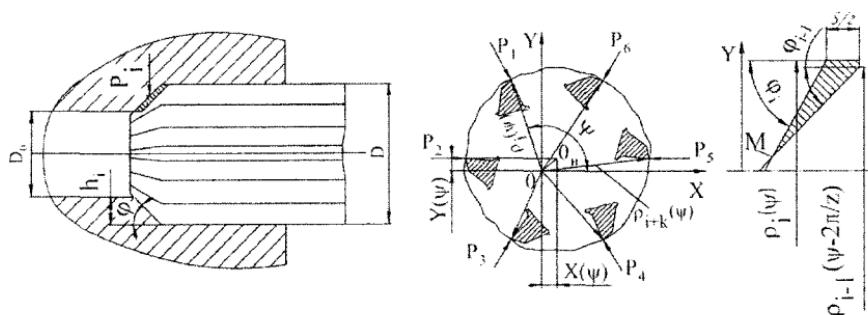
Расчетная схема для модели формообразования отверстий многолезвийными инструментами
